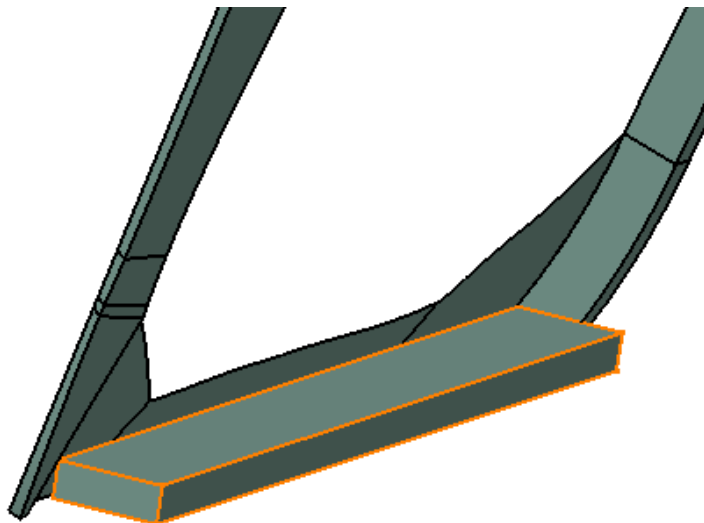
Sliding hood*: Unión soldada
